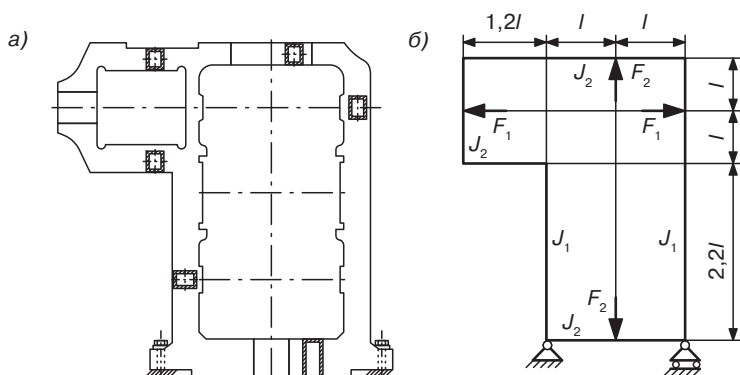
Схемы станины Г-образного каландра: а — схема конструкции; б — схема нагружения
